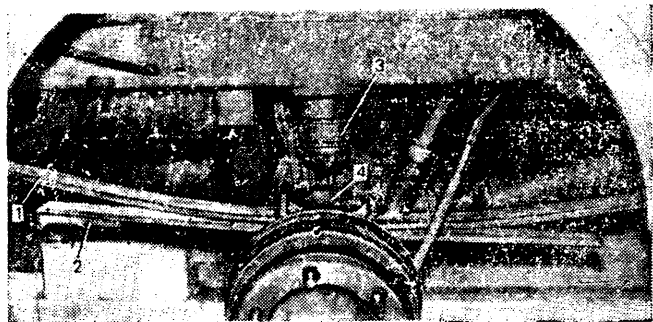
Задняя подвеска грузового автомобиля Фольксваген LT-35: 1 — основная рессора; 2 — дополнительная рессора; 3 — полый буфер; 4 — стальная чашка
